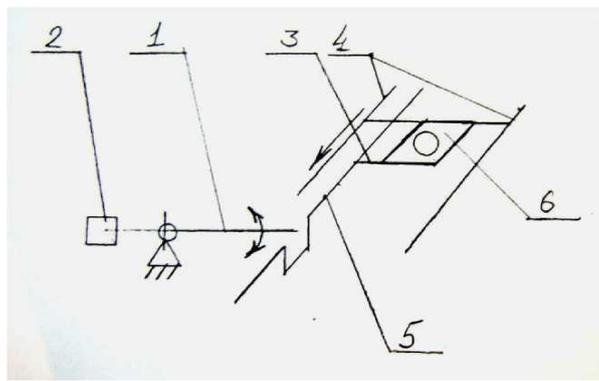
Технологическая схема весового калибровочного устройства: 1 - нож; 2 - груз; 3 - опорный палец; 4 - двухцепной транспортёр; 5 - направляющая; 6 - чаша
